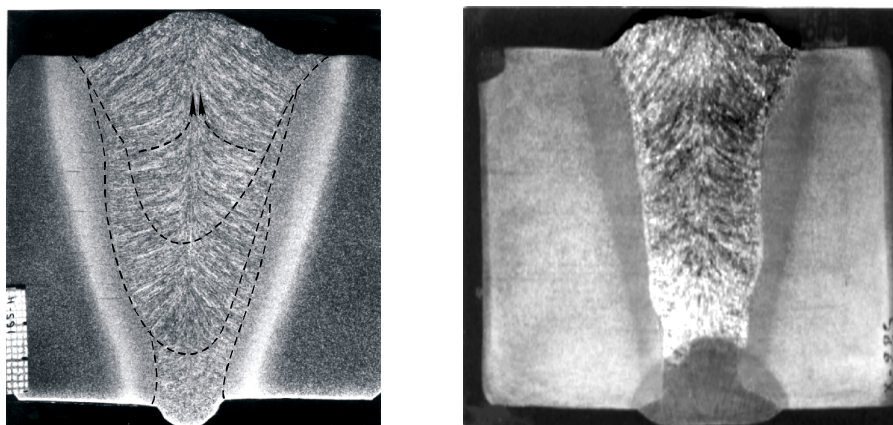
Макрошлифы сварных швов из стали 09Г2С толщиной 50 мм: а – с ППР по схеме II; б – с подварочным швом
